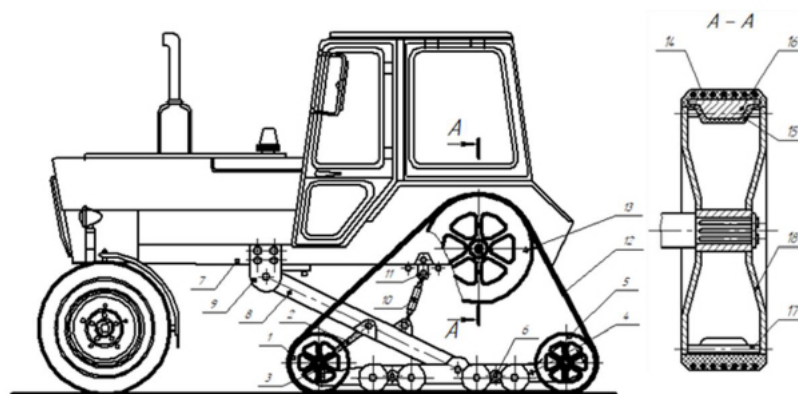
Полугусеничный движитель с резиноармированными гусеницами
